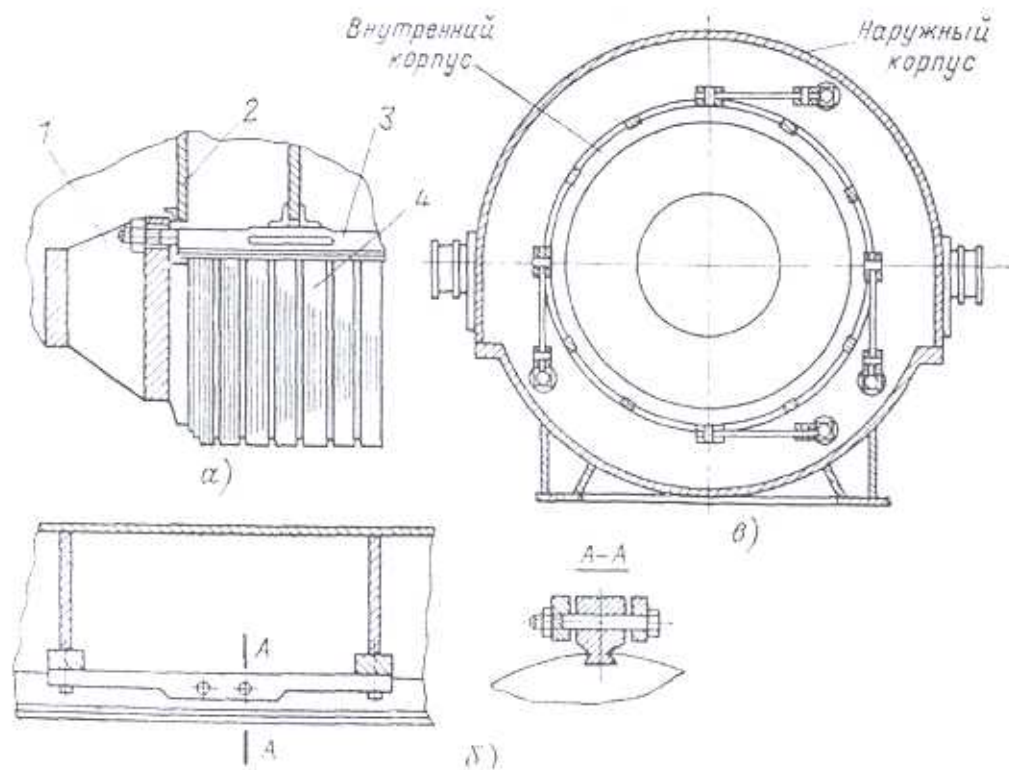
Упругая подвеска сердечника в корпусе статора:
